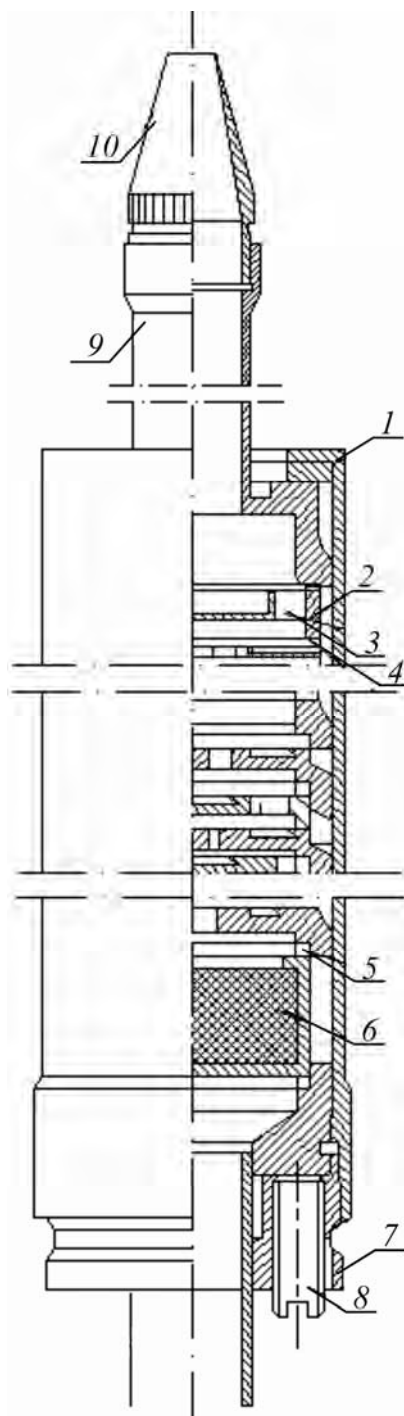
Схема импактора модели КИ-4: 1 — корпус; 2 — диски; 3 — сопла; 4 — выемка; 5 — фторопластовые прокладки; 6 — фильтр; 7 — накидная гайка; 8 — установочные болты; 9 — входной патрубок; 10 — сменный пылегазовый наконечник
